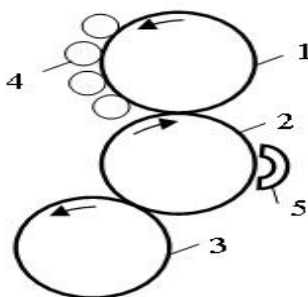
Схема расположения сушильного устройства: 1 – формный цилиндр; 2 – офсетный цилиндр; 3 – печатный цилиндр; 4 – накатные валики красочного и увлажняющего аппаратов; 5 – сушильное устройство
